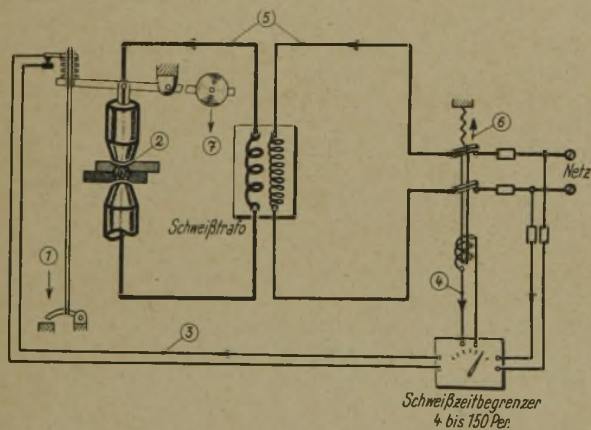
Elektrische Punktschweißung, Schweißstromsteuerung
